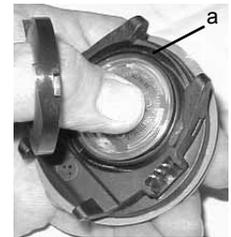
MISE EN PLACE DU COUVERCLE ET DE LA BAGUE
